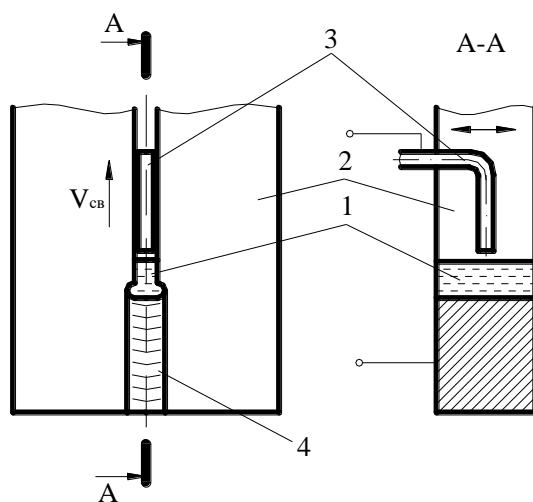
Схема процесса электрошлаковой сварки: 1 — шлаковая ванна; 2 — основной металл; 3 — сварочная проволока; 4 — сварной шов
